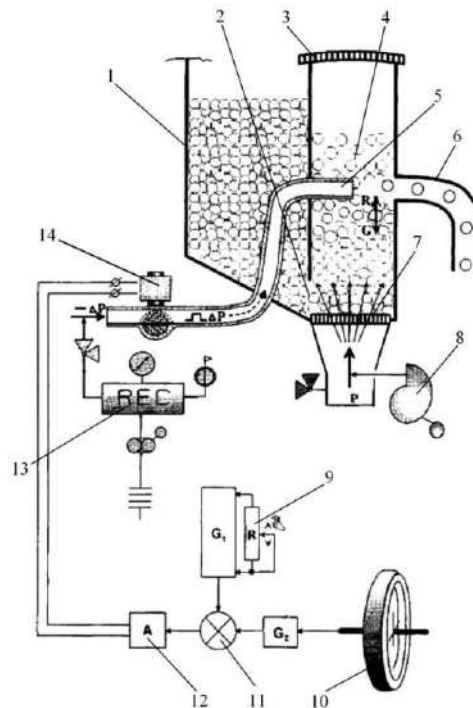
Пневмо-імпульсний висівний апарат [38]: 1 – бункер; 2 – живильна камера; 3 – решітка; 4 – робоча камера; 5 – ежекторний патрубок; 6 – насіннєпровід; 7 – дека; 8 – вентилятор; 9 – регулятор норми висіву; 10 – колесо; 11 – суматор; 12 – підсилювач; 13 – ресивер; 14 – електромагнітний клапан
